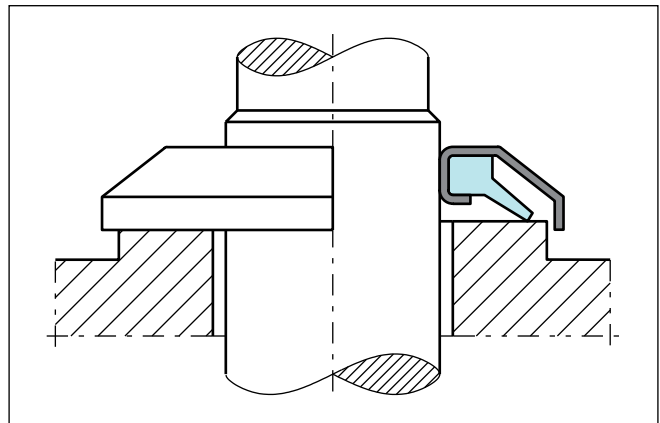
Ausführung der Lauffläche für senkrechte Wellen
